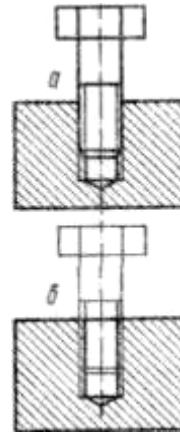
Читання креслення деталей, з'єднаних різьбою
